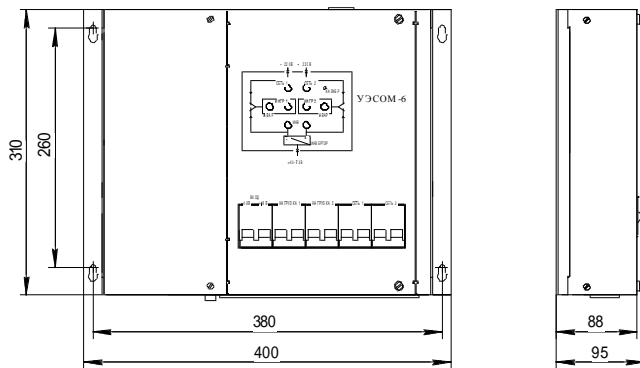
Габаритный чертеж УЭСОМ-6
